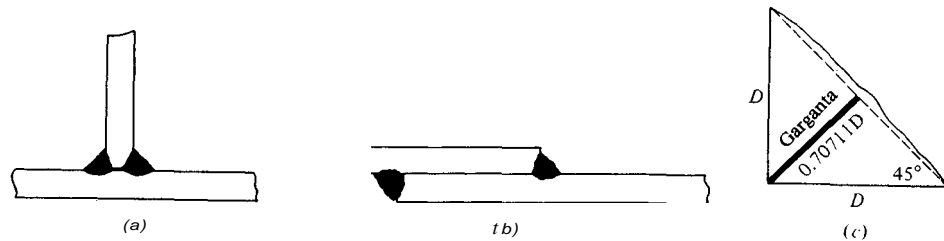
Área crítica de cortante para soldaduras de filete. a) Soldadura de filete para junta te. b) Soldadura de filete para junta traslapada. c) Dimensión en la garganta para área mínima de cortante.
